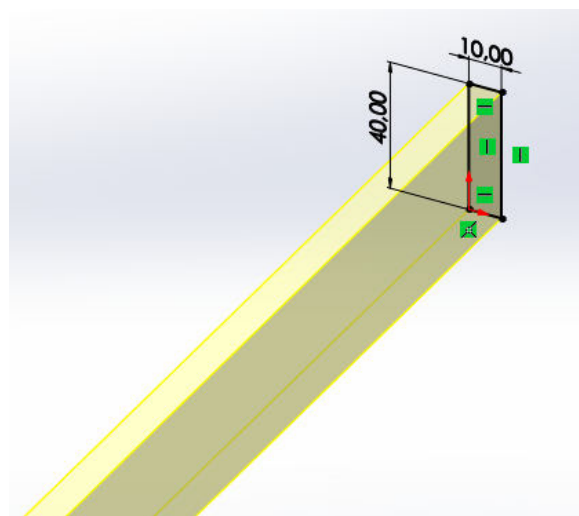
Croquis del refuerzo aportado para el perfil en C.
